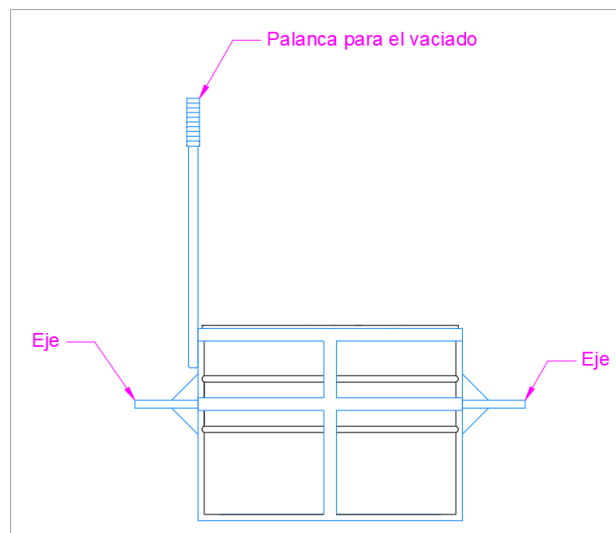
Disposición de ejes soldados a la canastilla, vista frontal.
